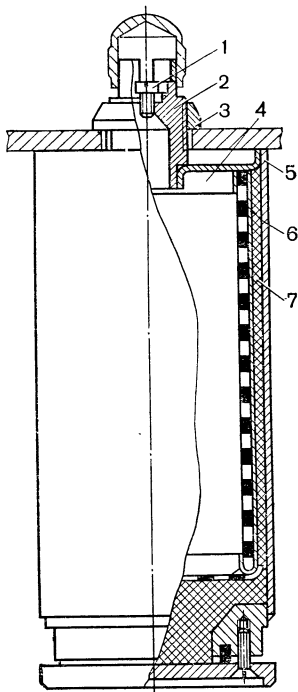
Общий вид полевой установки ПУВИГ для ввода в кабель индикаторного газа
